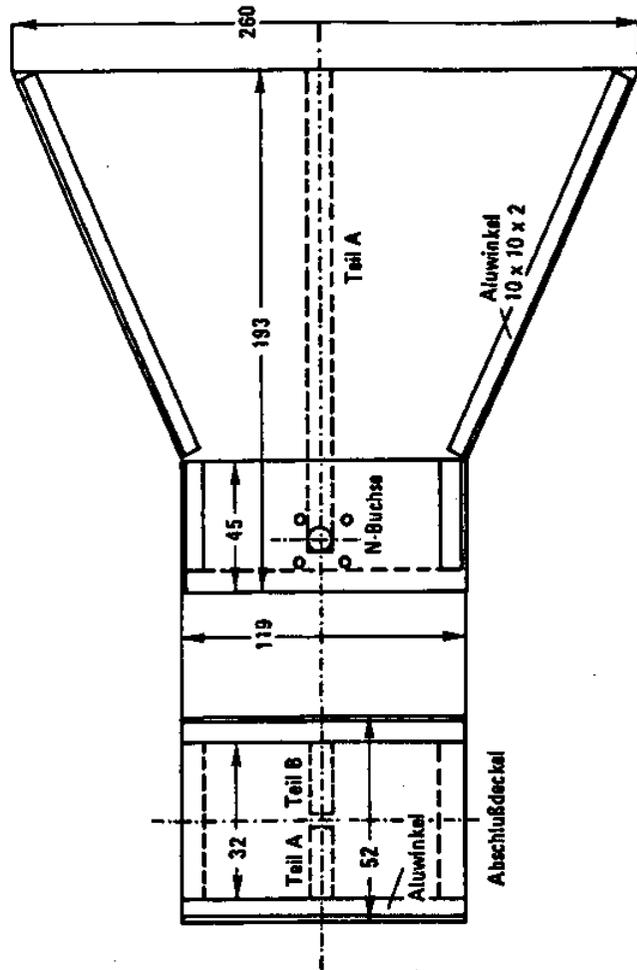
Seitenteile E und F zum Universal-Strahler.
